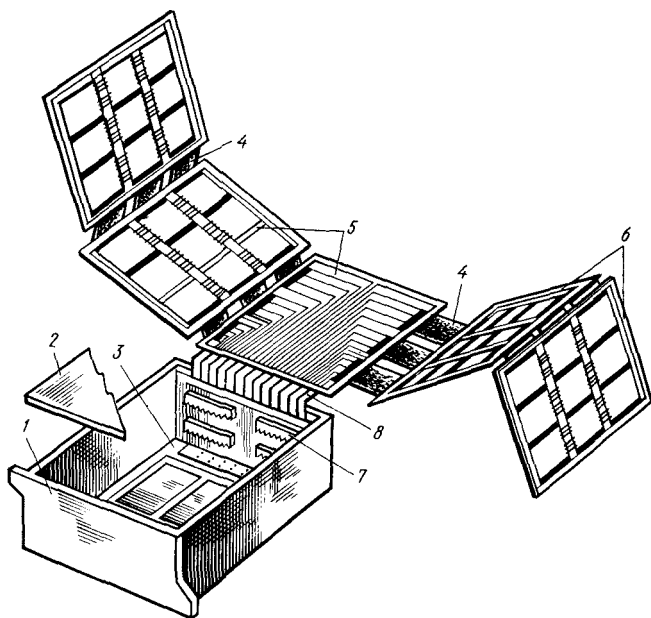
Общий вид блока бортовой ЭВМ:
